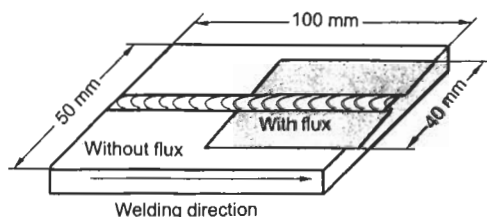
镁合金 AZ31B 试样 TIG/A-TIG 焊接示意图
